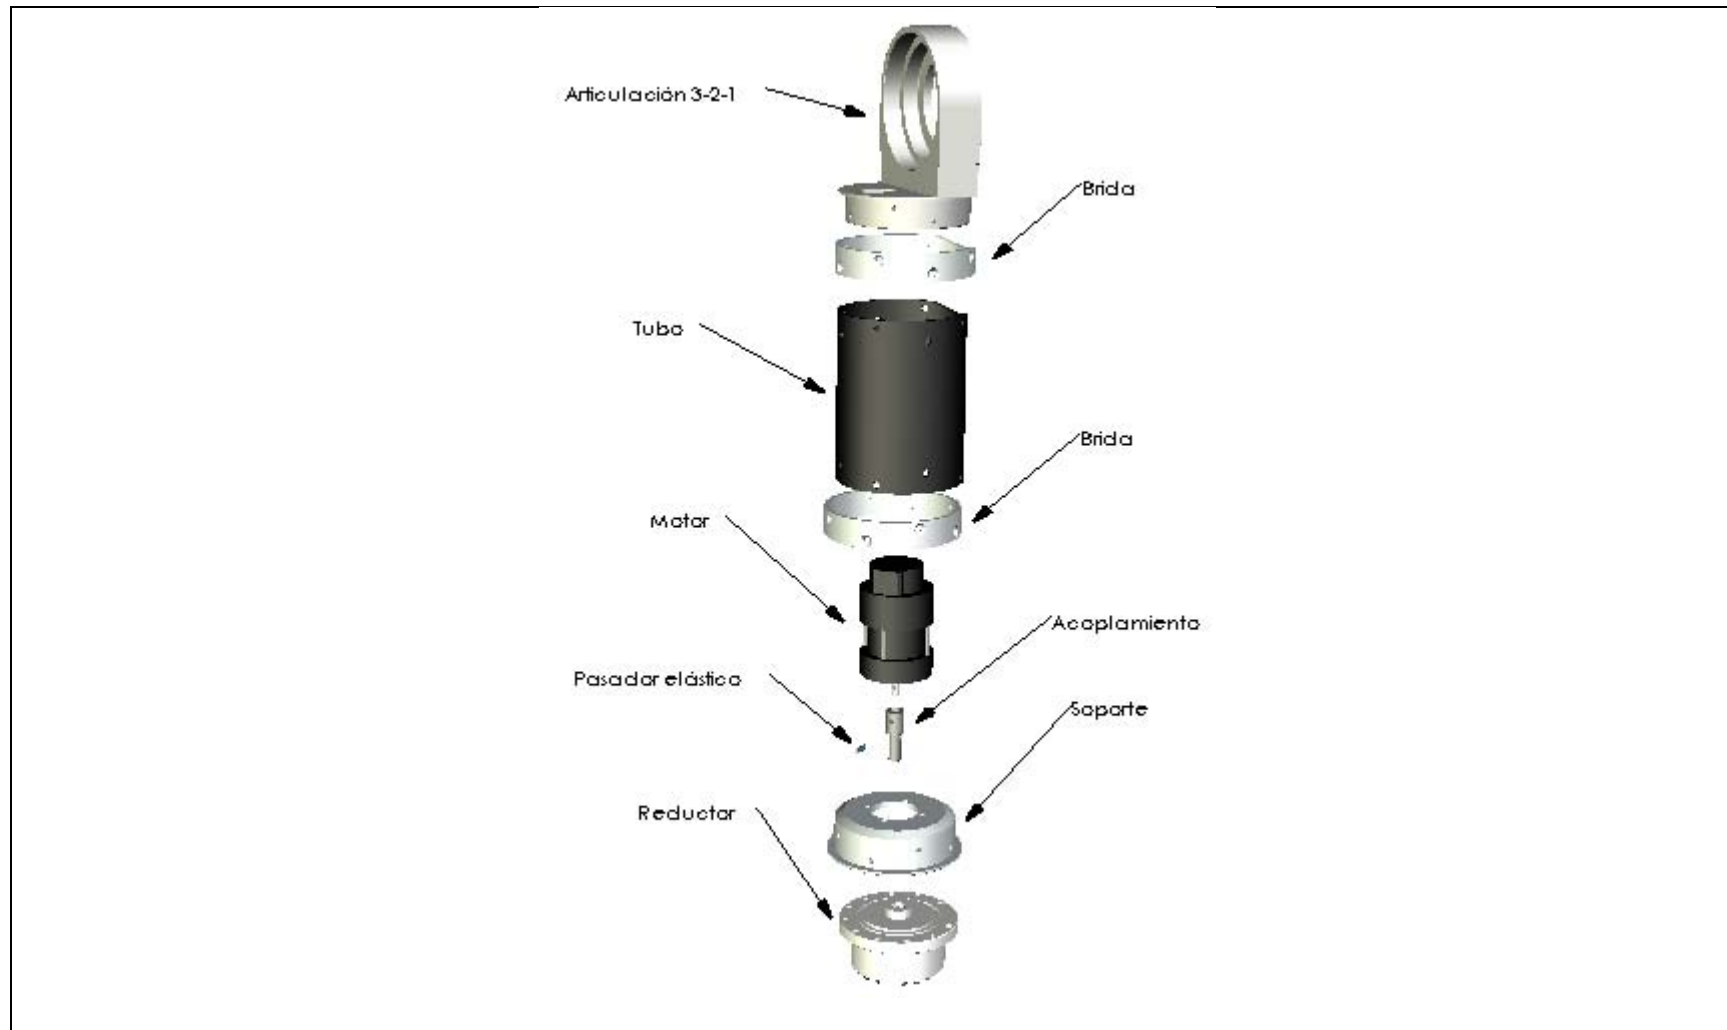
Vista explosionada del sub-ensamblaje 2.
